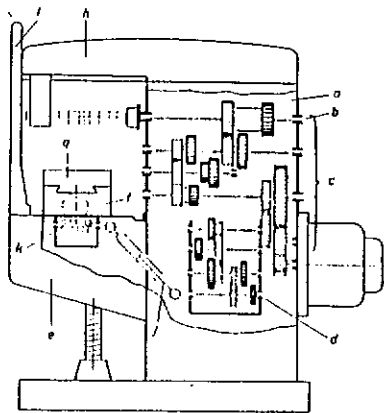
(arriba). Máquina fresadora horizontal.
